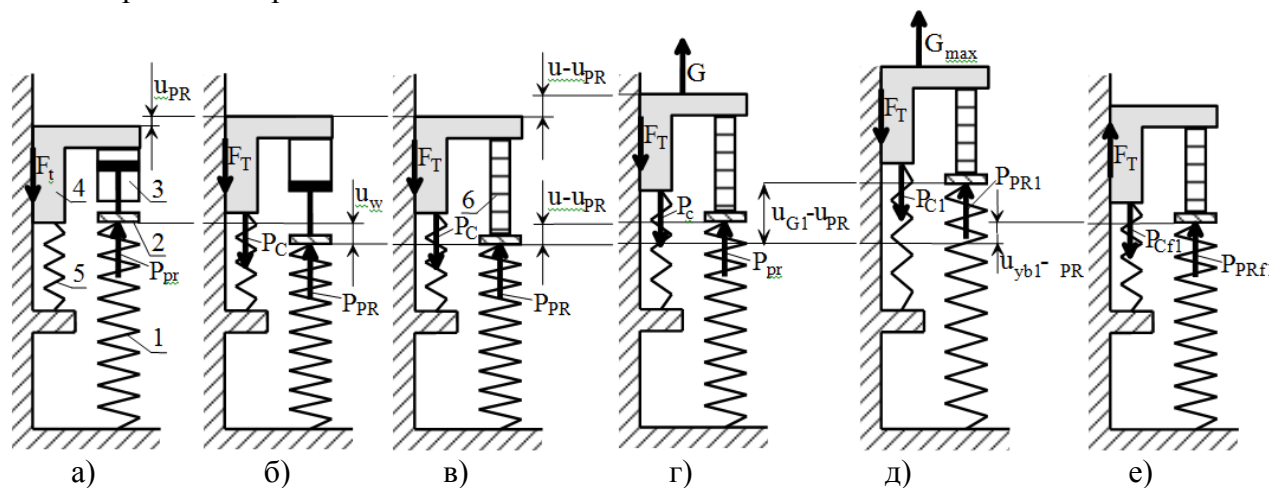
Процесс запрессовки обмоток, подъема и опускания а.ч.
